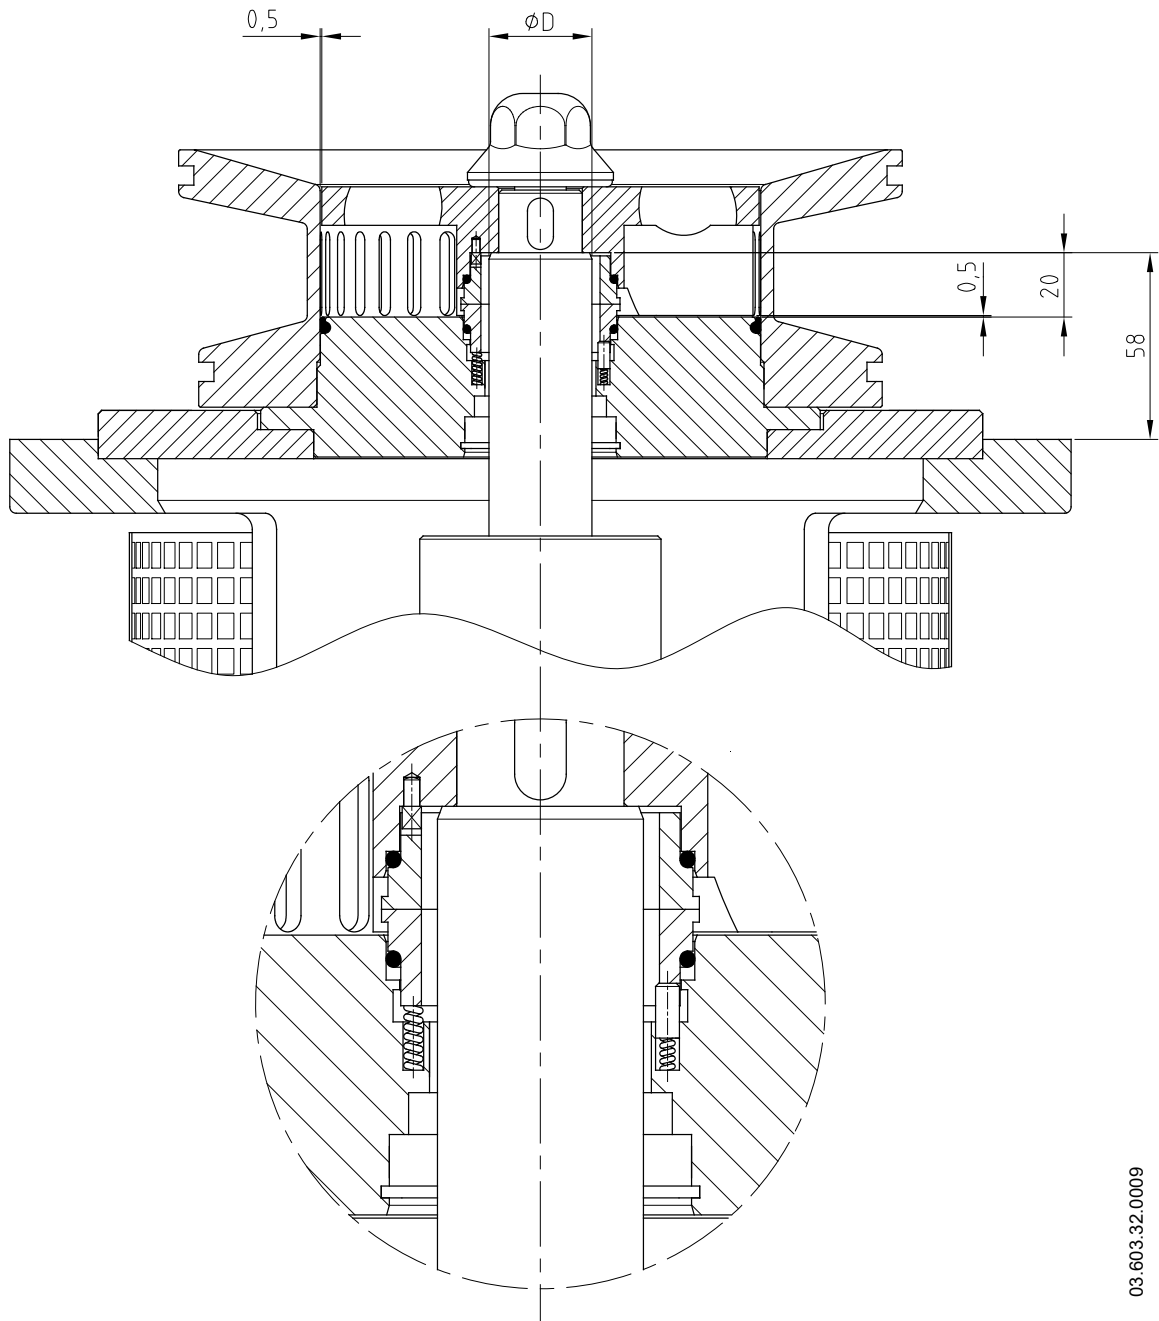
Dimensions de montage pour la taille ME-6103/6105/6110 RE.
